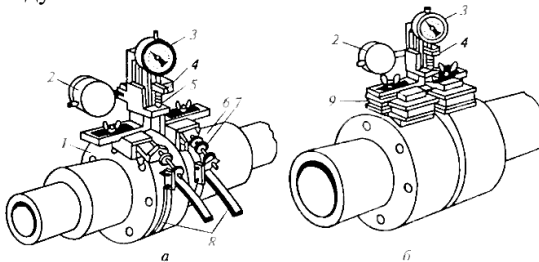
Приспособления для центровки валов: а — с ленточным прижимом; б — с электромагнитным прижимом: 1 и 6 — пол у муфты; 2 и 3 — индикаторы; 4 — держатель; 5 — измерительный стержень; 7 — натяжное устройство; 8 — стальная лента; 9 — электромагнит.
